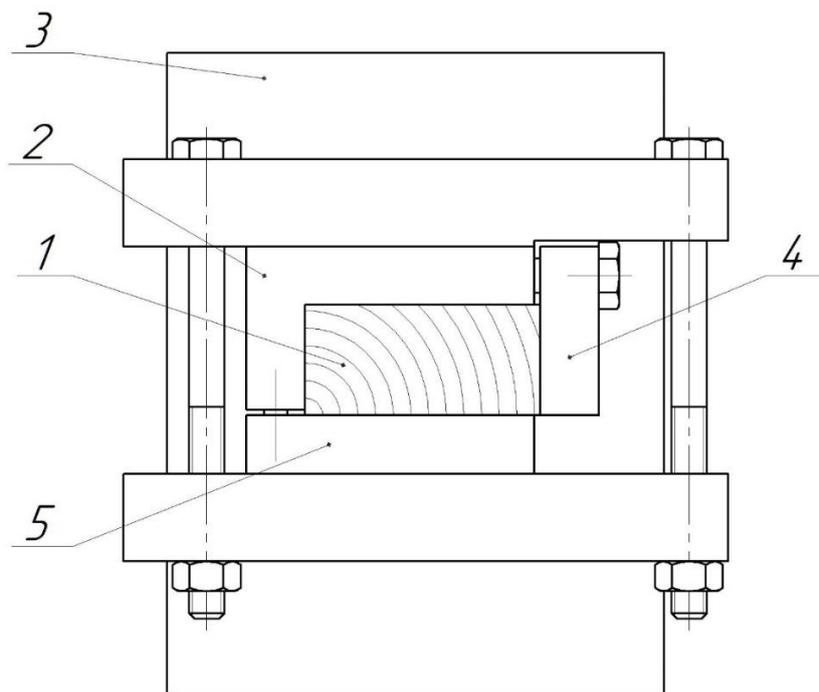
Предварительная конструкция зажимной матрицы (вид сверху)
